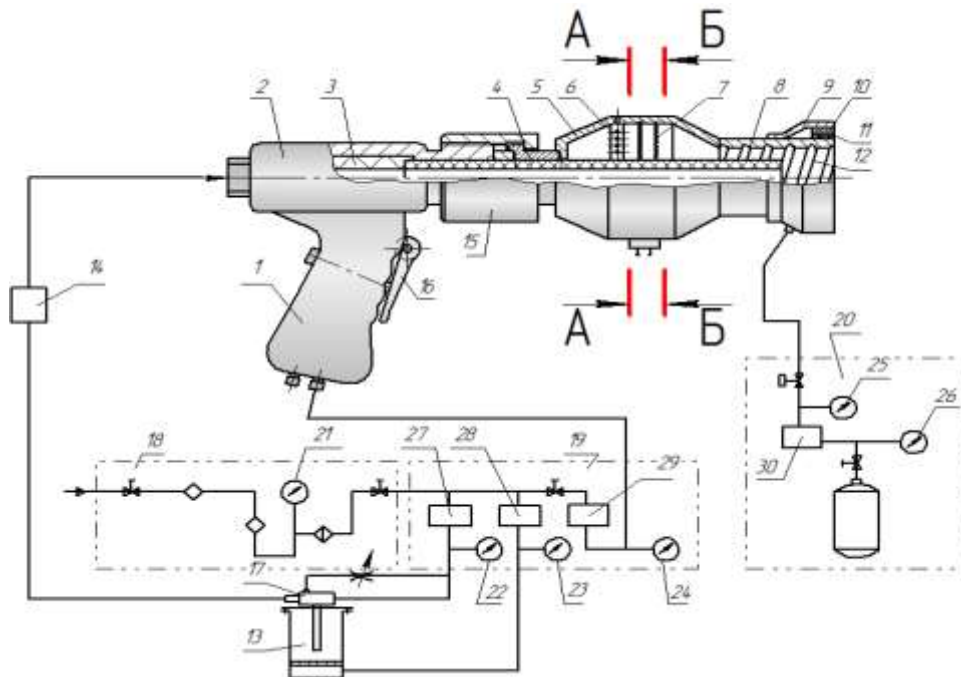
Устройство для нанесения покрытий комбинированным электрогазоплазменным способом: 1 – рукоятка; 2 – зарядный элемент; 3 – ствол; 4 – керамическая трубка; 5 - корпус узла нагрева; 6 – тороидальный коллектор; 7 – проволочные нагреватели; 8 – выходной насадок; 9 – корпус инфракрасного излучателя; 10 – керамическое кольцо инфракрасного излучателя; 11 – отверстия в керамическом кольце; 12 – винтообразные канавки; 13 – порошковый питатель; 14 – узел предварительного нагрева; 15 – муфта присоединительная; 16 - курок; 17 – эжекторный насос; 18 - блок подготовки воздуха; 19 – пневматическая панель; 20 – газовый блок; 21, 22, 23, 24 -манометры; 27, 28, 29, 30 - регуляторы давления.
